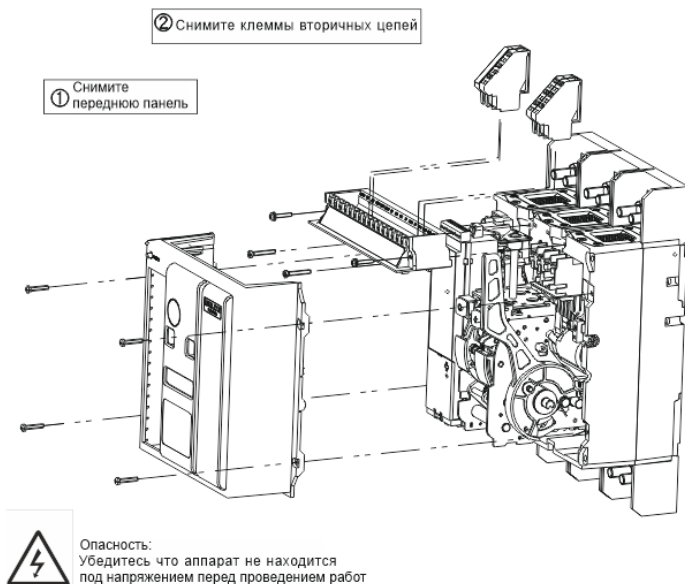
Схема установки аксессуаров внутрь корпуса для аппарата ВА-338Е
